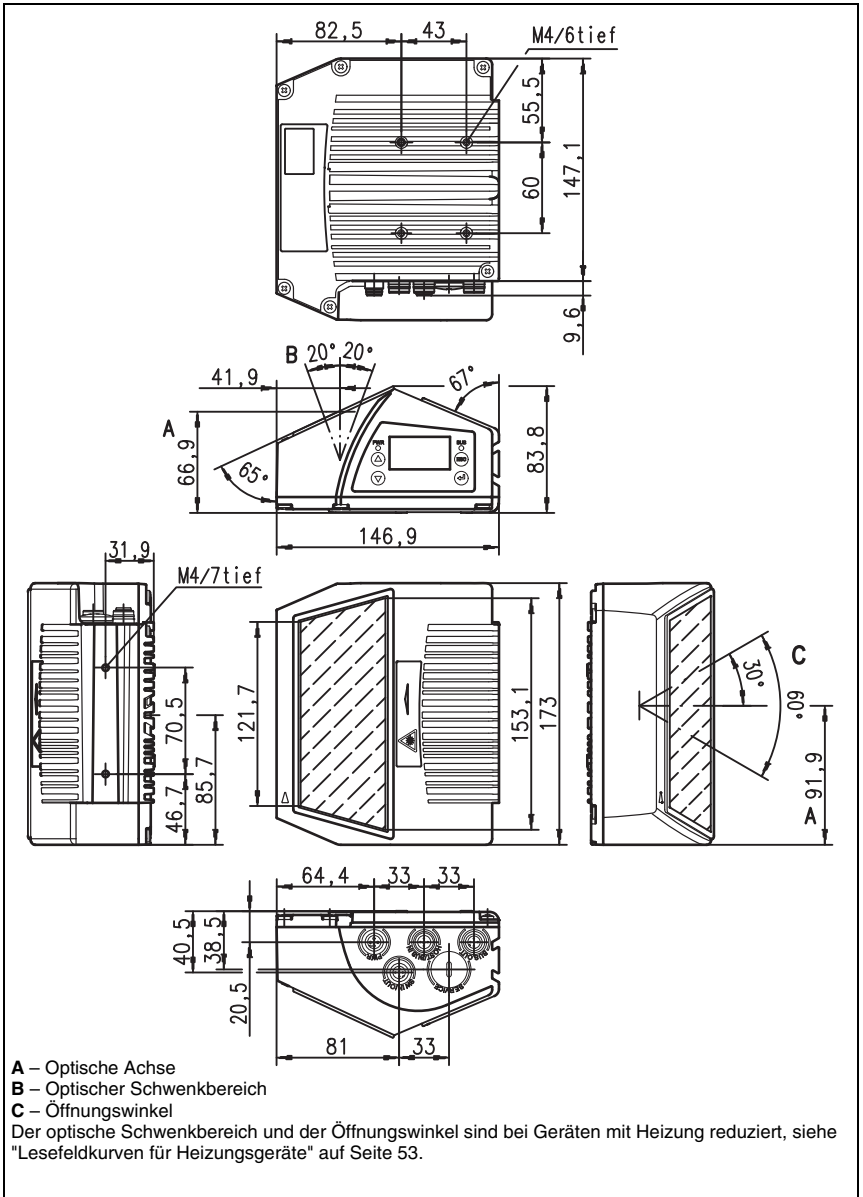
Maßzeichnung Scanner mit Schwenkspiegel BCL 508*i*/O...100
